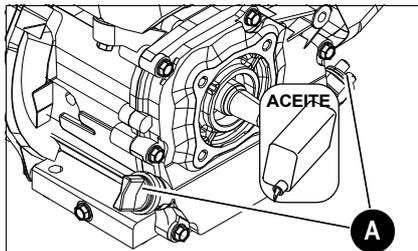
Rellenar aceite de motor (motor de gasolina)
